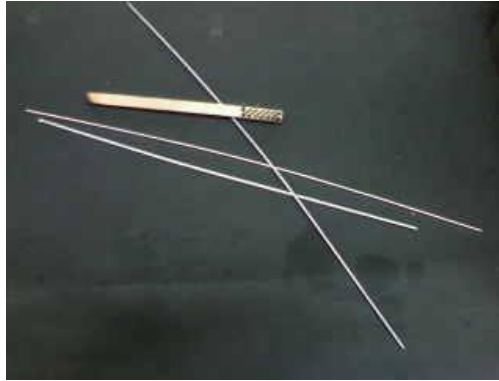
Soldadura para aluminio DURAFIX.
